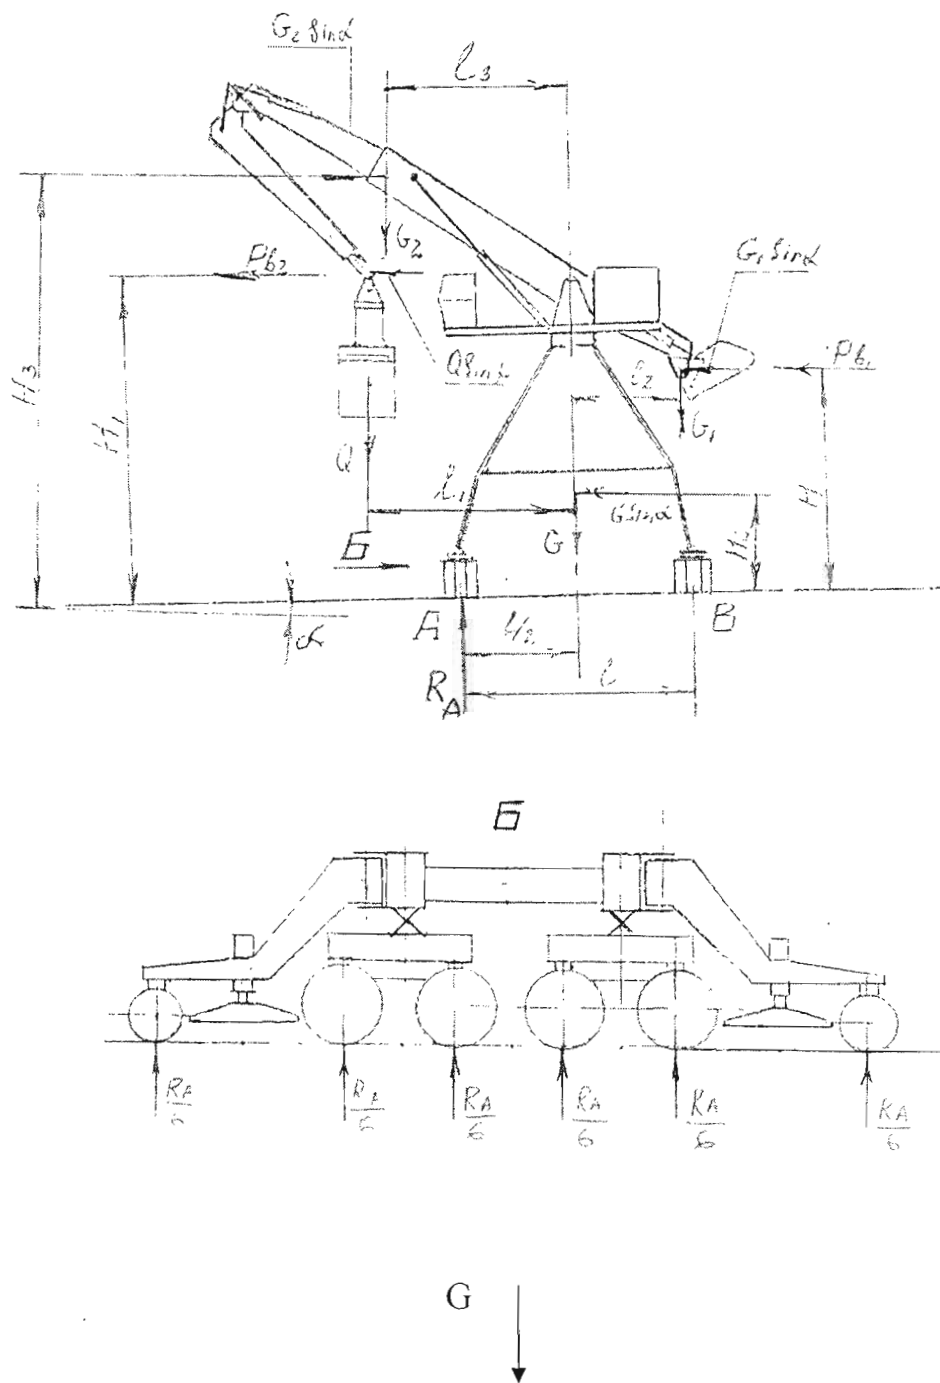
Расчётная схема для определения нагрузок на колёса ходовых гележек и колёса выносных опор при передвижении крана с поднятым грузом
